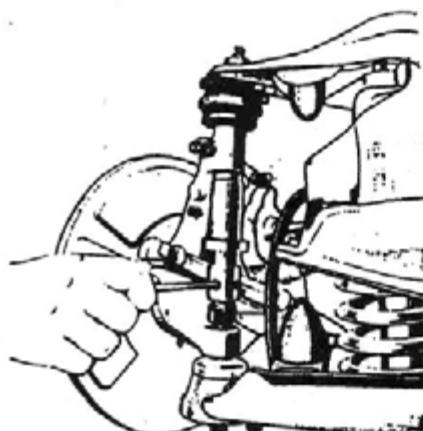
Выпрессовка конуса пальца шаровой опоры
